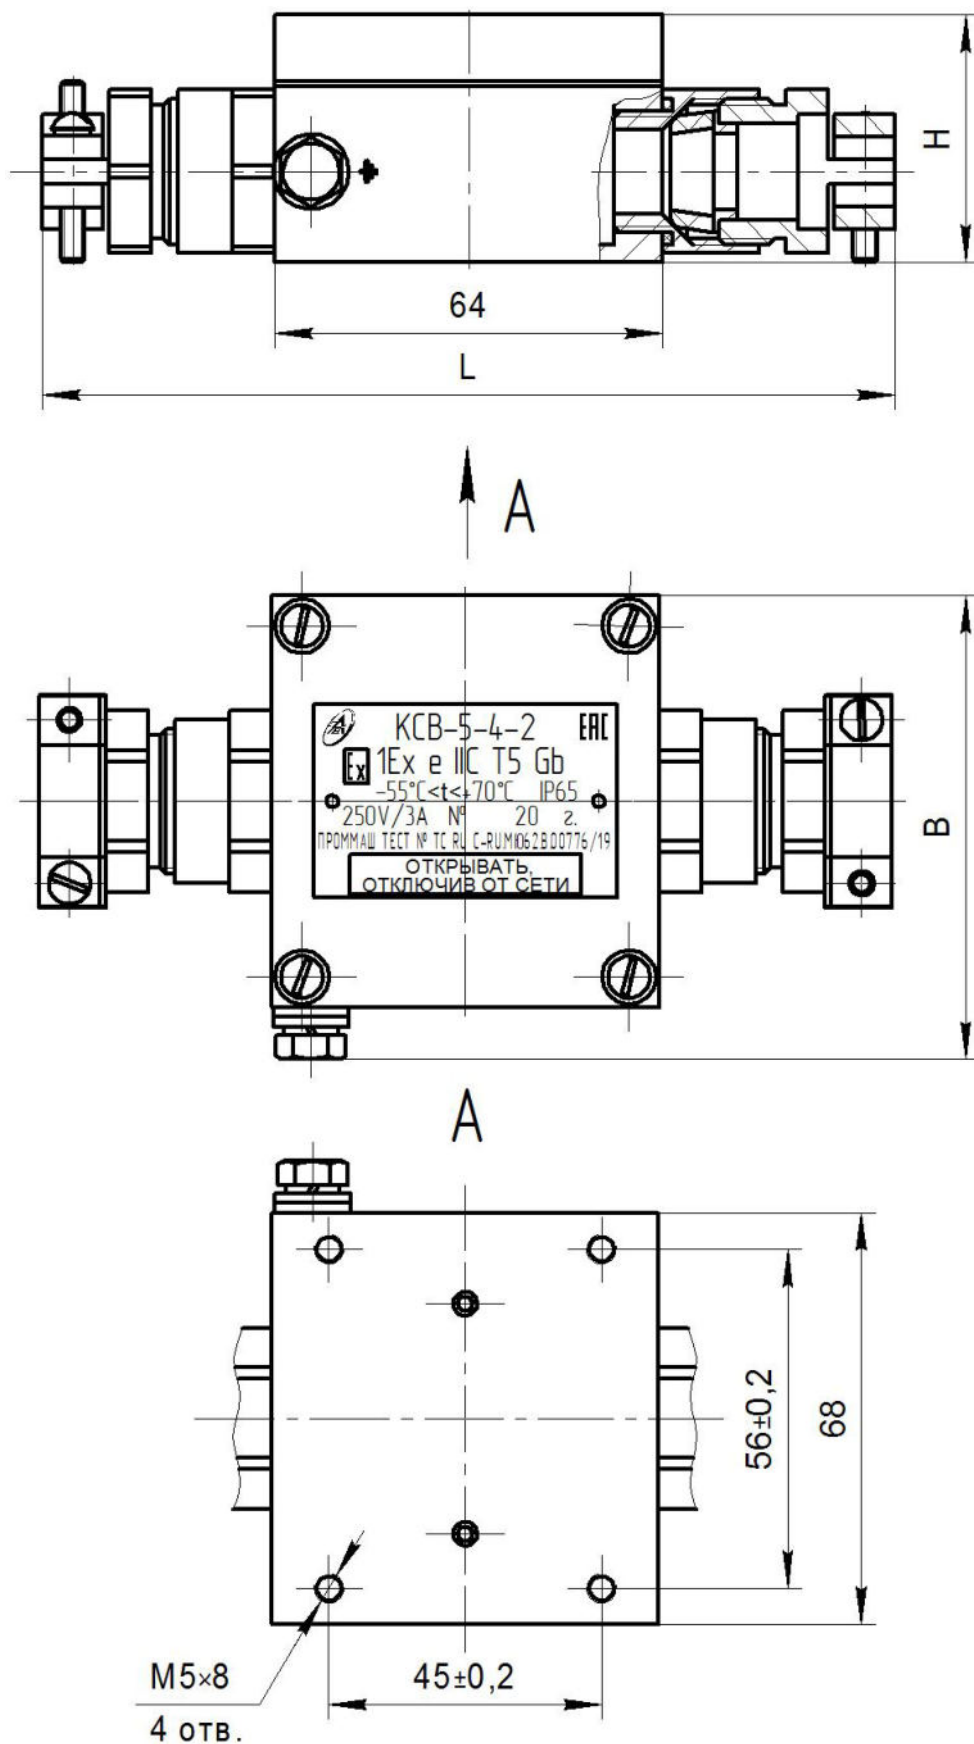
Внешний вид и присоединительные размеры коробки КCB-5-4-2
